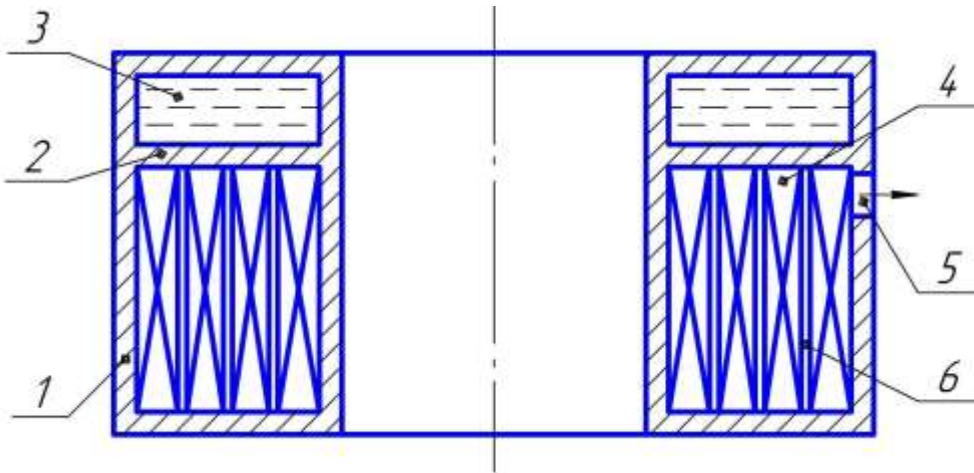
Конструкція котушки з охолодженням обмотки за принципом парової камери: 1 – металевий корпус; 2 – щочки; 3 – камери для охолодження проточною водою; 4 – робочий об'єм; 5 – отвір; 6 – паропроводи
